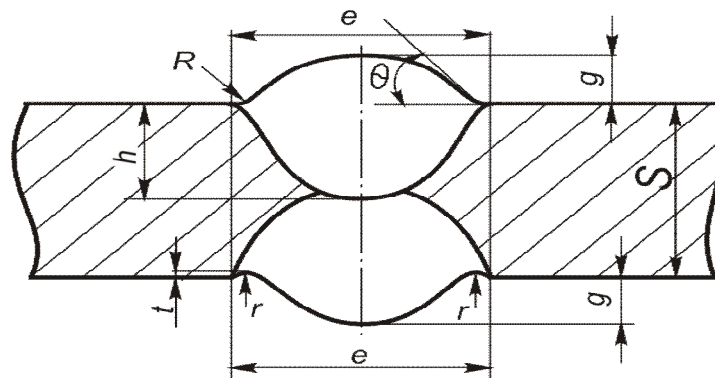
Поперечное сечение шва при сварке стыковых соединений
